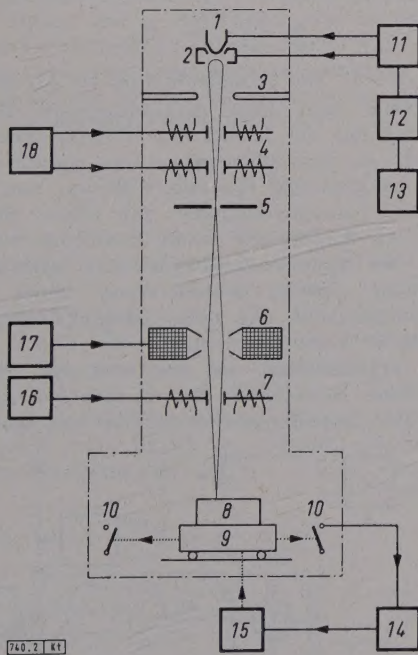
Grundsätzlicher Aufbau einer Elektronenstrahl-Schweißmaschine.
